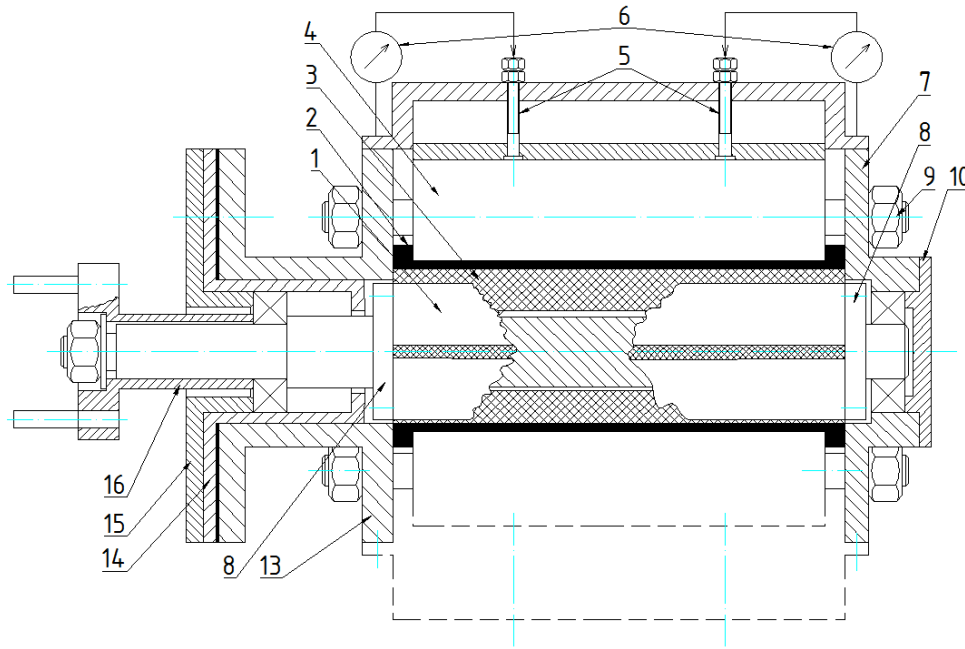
Опытный образец РПМ с магнитным отжимом пластин.
